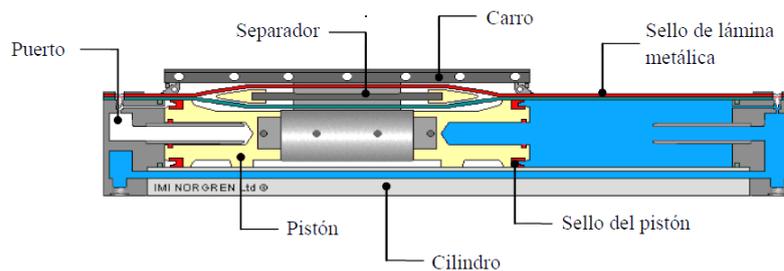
Vista esquemática de un cilindro sin vástago del tipo carro – pistón.
